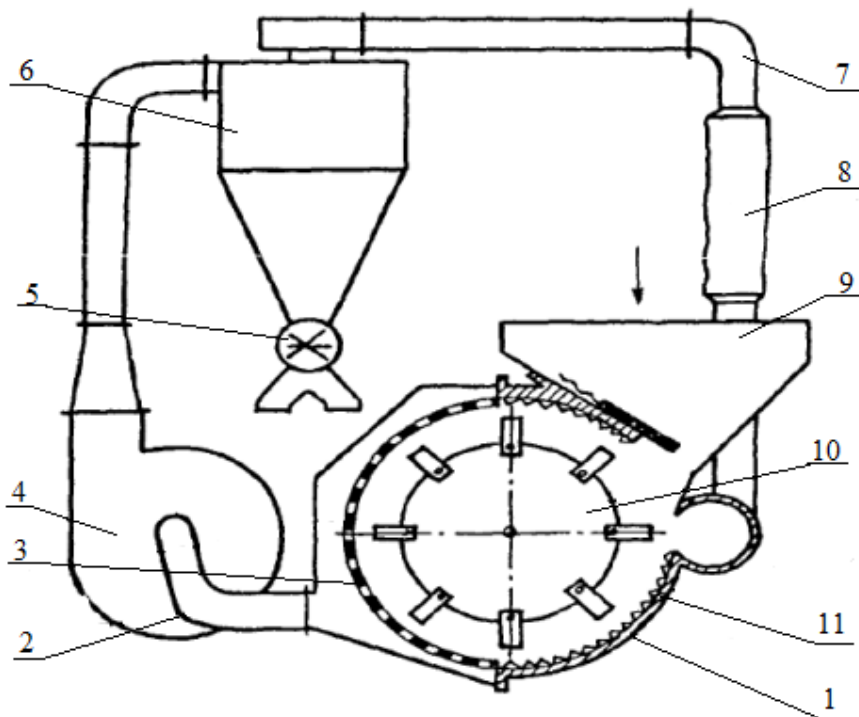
Схема кормодробарки КДМ-3,0: 1 – корпус; 2 – подвійний патрубок; 3 – решета; 4 – вентилятор; 5 – шлюзовий затвор; 6 – циклону; 7 – трубопровід; 8 – фільтр; 9 – бункер; 10 – дробильний барабан; 11 – деки.
